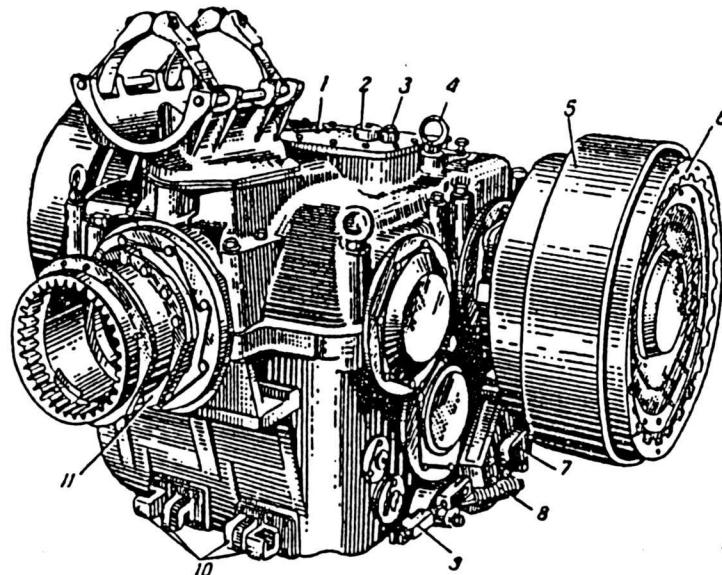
Коробка передач с механизмами поворота (общий вид спереди):
